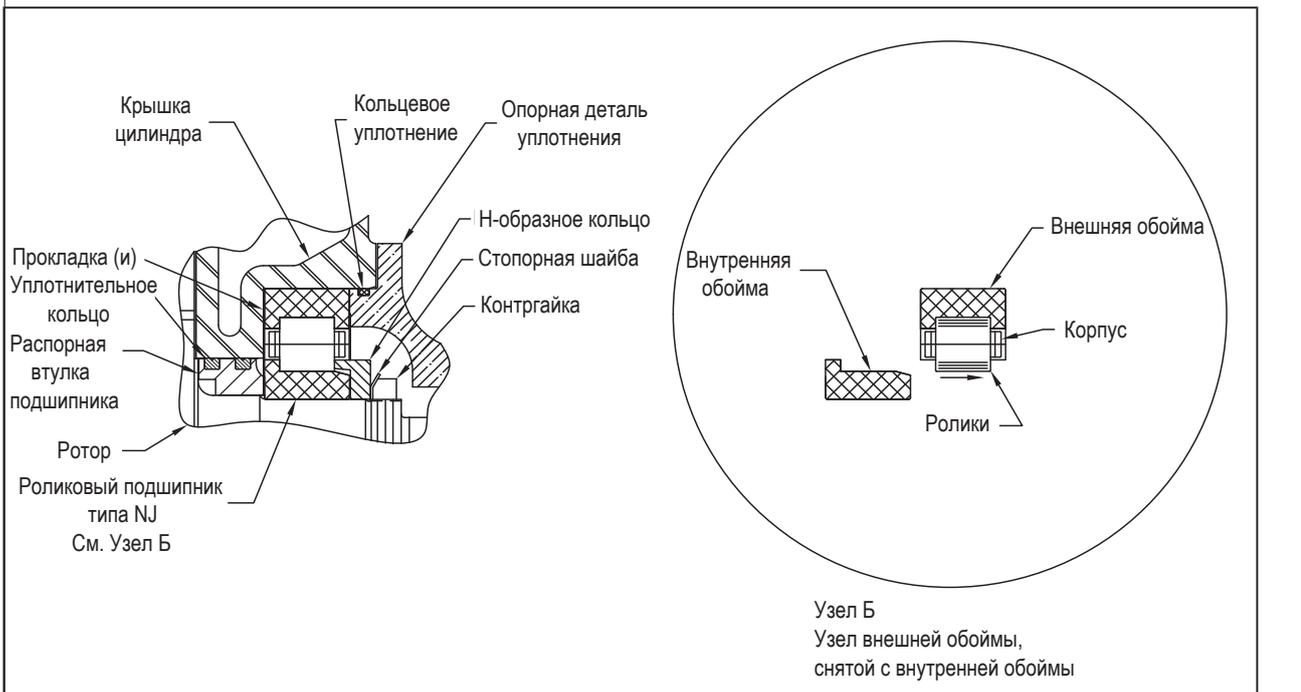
Узел Н-образного кольца, стопорной шайбы, контргайки и роликового подшипника.
